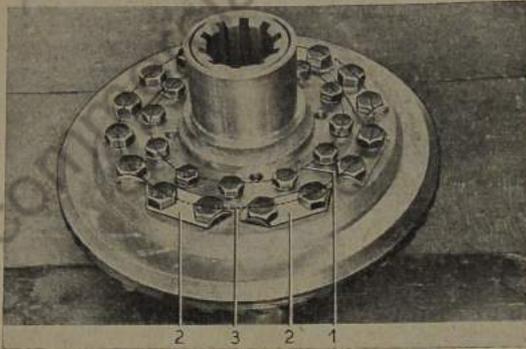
Tellerrad am Bund des Ausgleichgehäuses anschrauben
